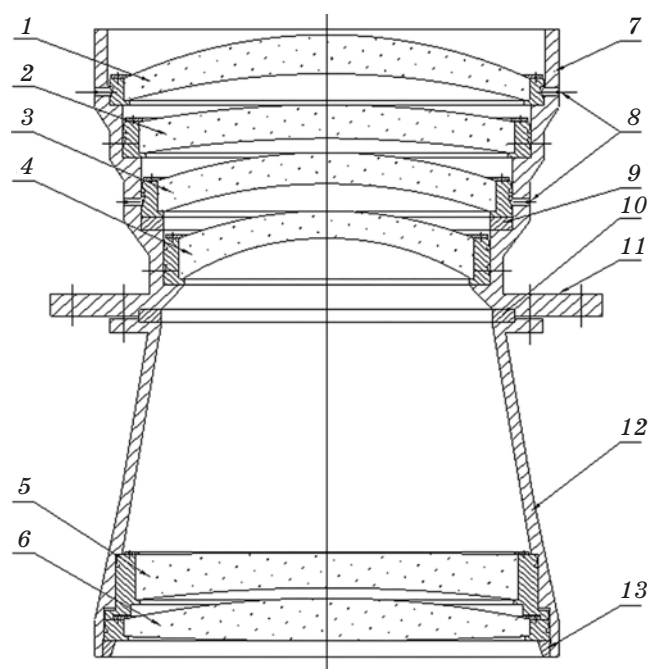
Конструкция объектива. 1–6 — линзы в оправе, 7 — первый полукорпус, 8 — юстировочные винты, 9 — промежуточное кольцо, 10 — межкорпусное промежуточное кольцо, 11 — посадочный фланец, 12 — второй полукорпус, 13 — прижимное кольцо
